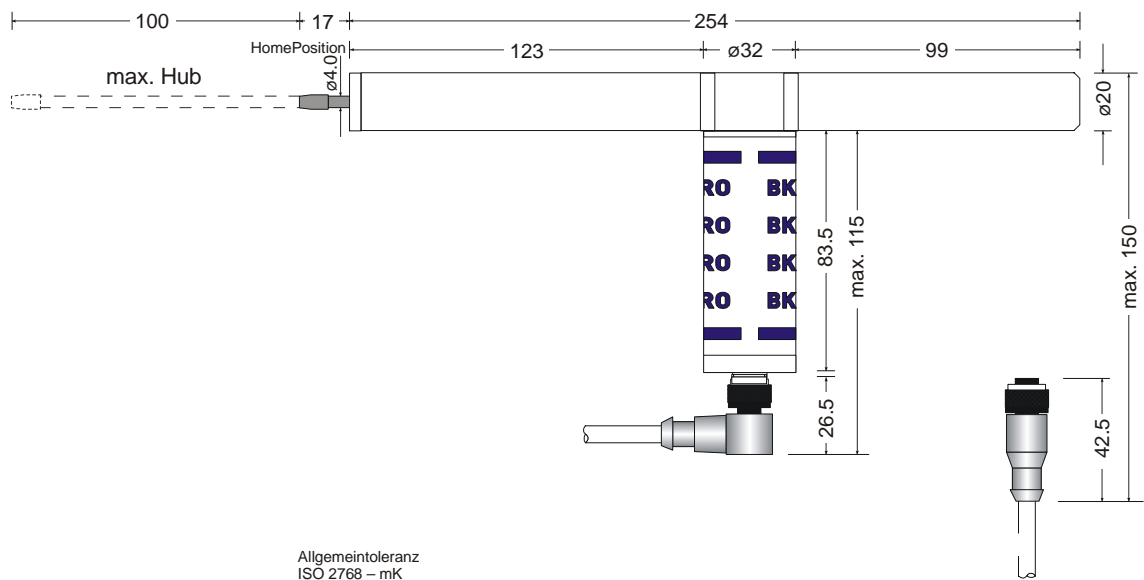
Mechanische Abmessungen – Tastkopf TK9LIN100
